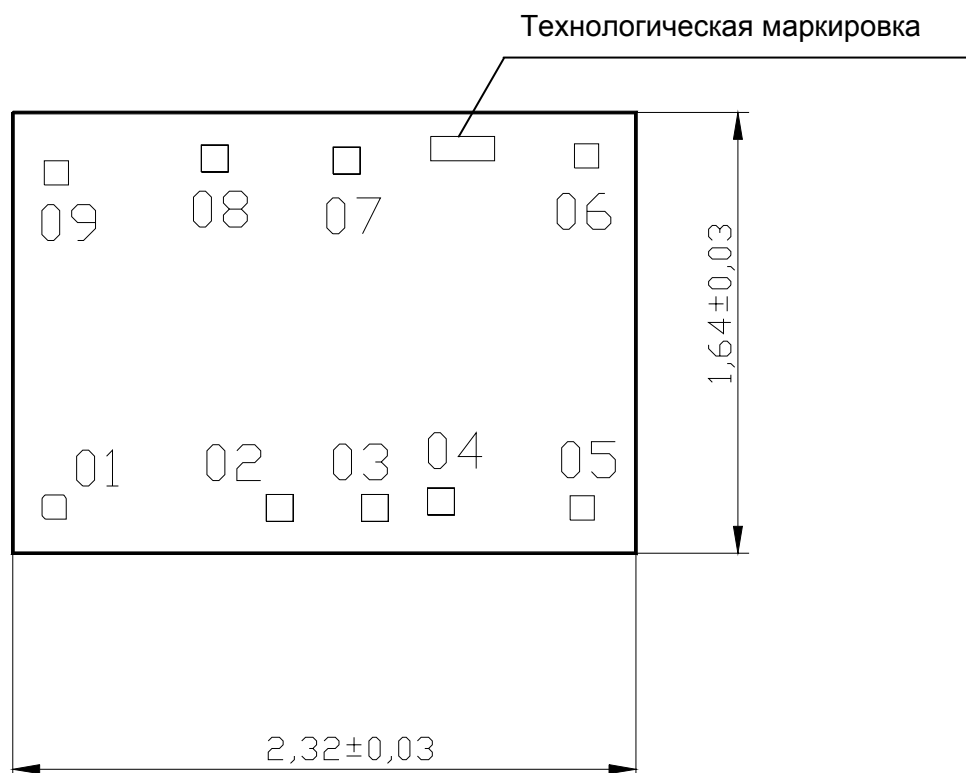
Габаритные размеры корпуса MS-012AA
